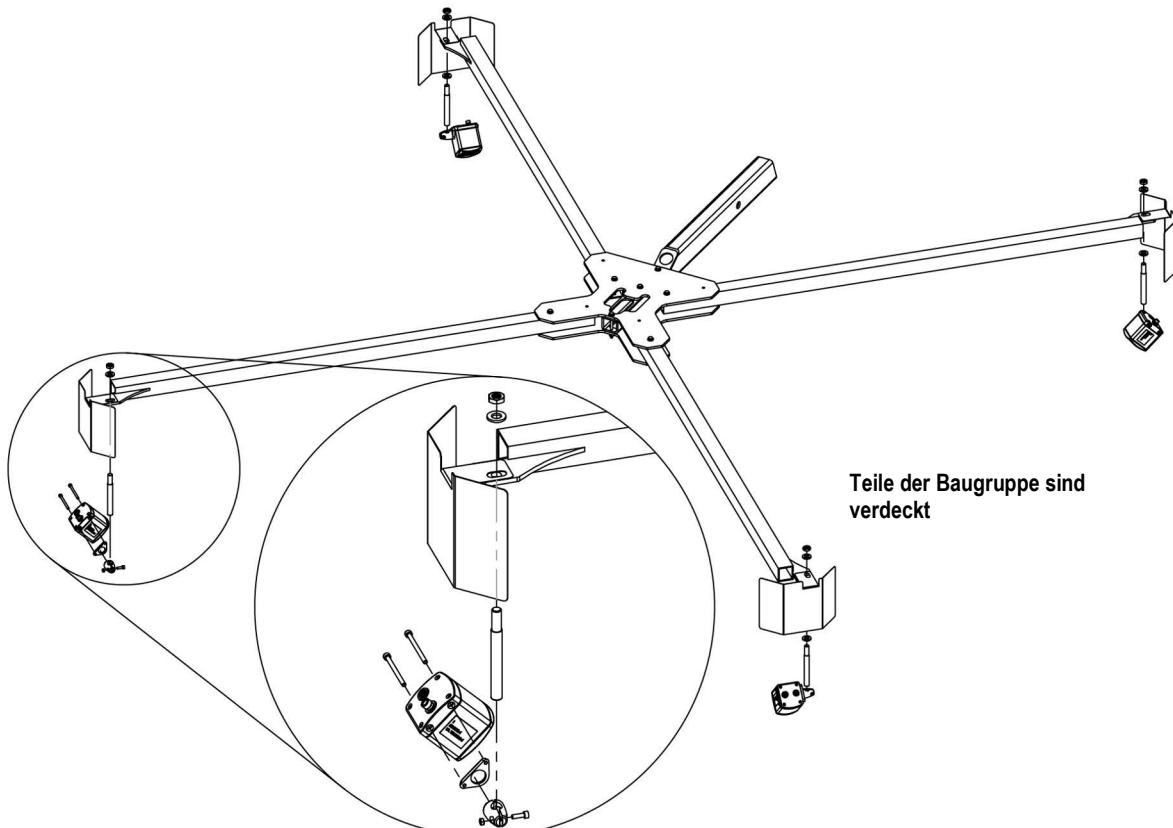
Montage der Schutzvorrichtungen für den Remote-IFM-Sensor
